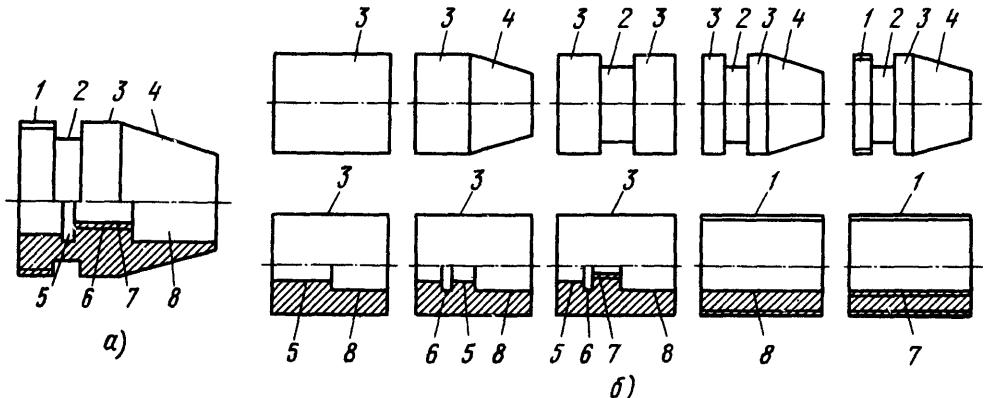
Комплексная (а) и другие детали (б) группы для токарной обработки:
